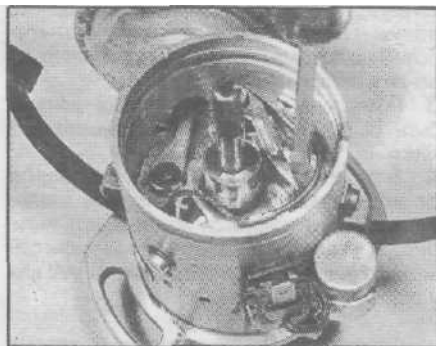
, б. Регулировка зазора между контактами прерывателя
